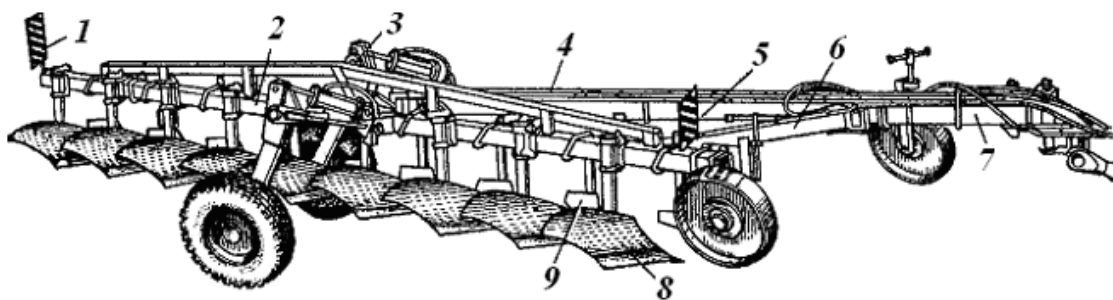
Плуг напівначіпний дев'ятикорпусний ПТК-9-35: 1 - сигнальний щиток; 2 - основний брус; 3 - транспортний механізм; 4 - маслопроводи; 5 - поздовжній брус; 6 - поперечний брус; 7 - начіпний пристрій; 8 - корпус; 9 - передплужник
